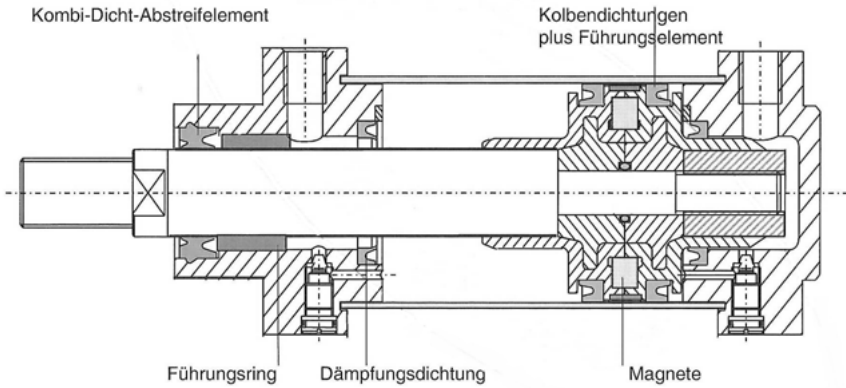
Typisch aufgebauter Pneumatikzylinder
